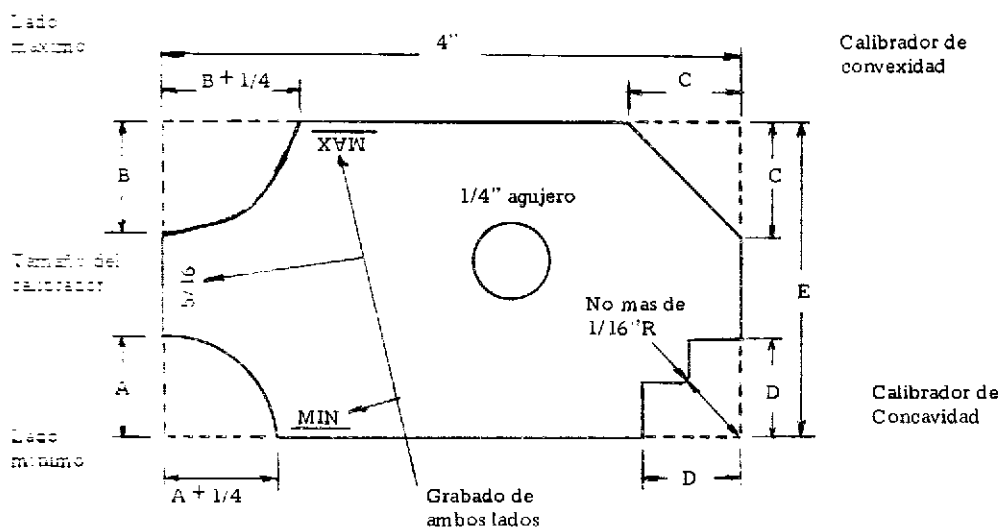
Calibrador típico de soldaduras de filete.
